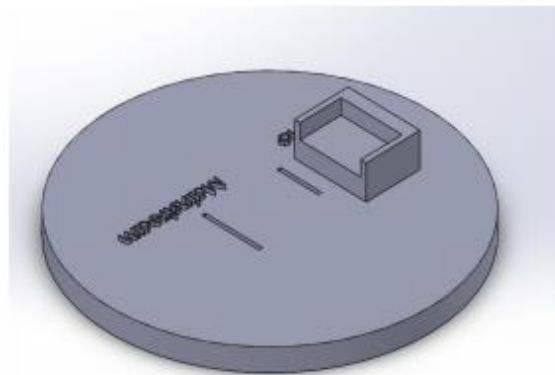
Fixture para operación de soldadura de L Flex, vista 2.
